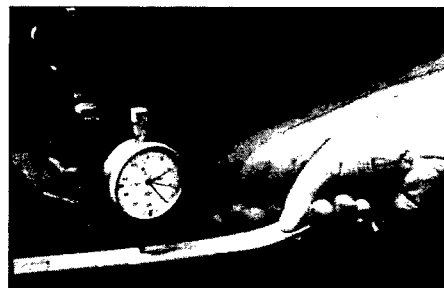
Da sich metallgefüllte Elastomere nicht sehr verformen (außer bei Hohlquerschnitten), darf die Dicke nicht außerhalb der Toleranzgrenzen liegen. Zu hohe Abweichungen in der Dicke verschlechtern die Abdichtungseigenschaften.
